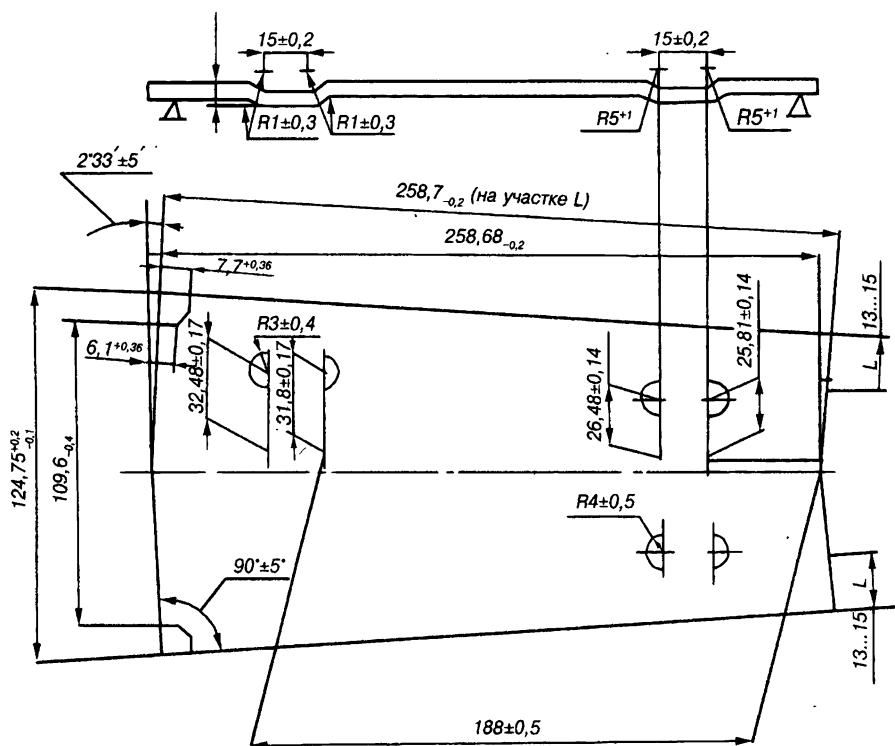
Схема вырубki и рельефной штамповки профиля развертки короба на прессе K1128 с усилием 630 кН.
